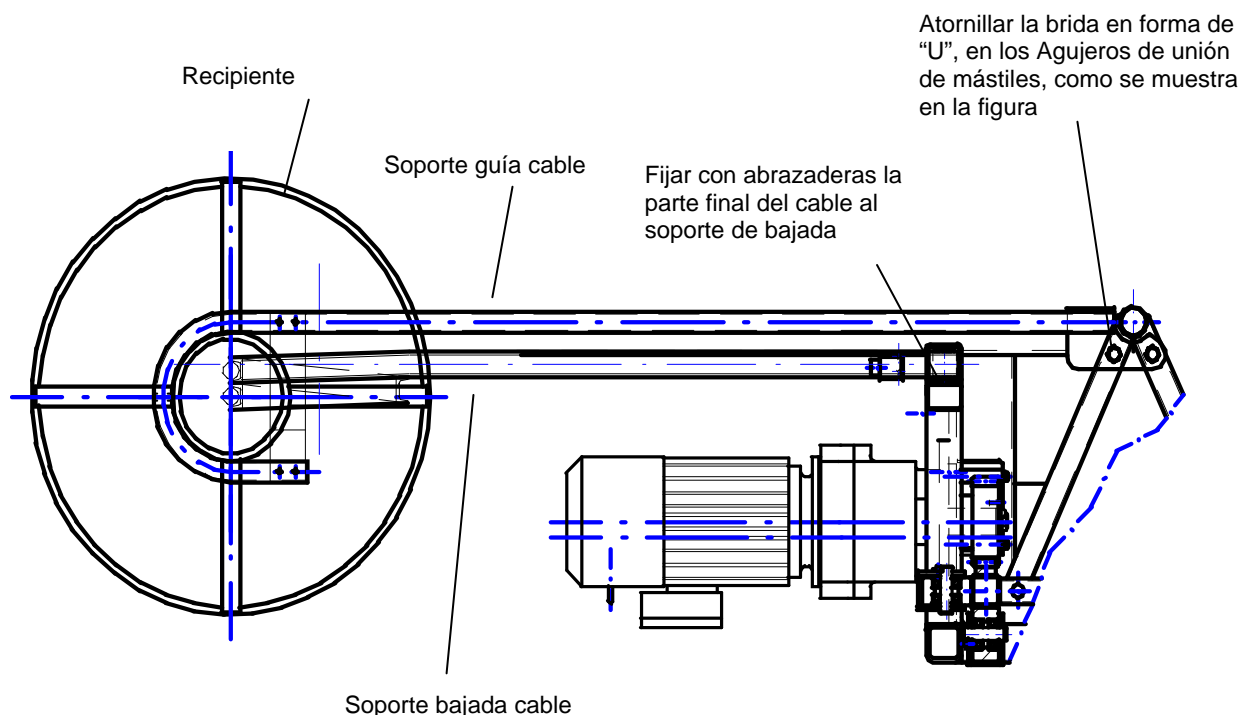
Montaje Guía Cable Mástil Triangular
